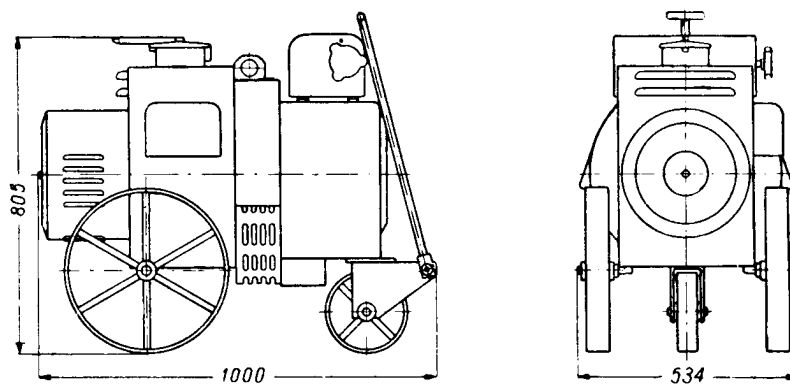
Massbild des Schweissumformers EW-21u
